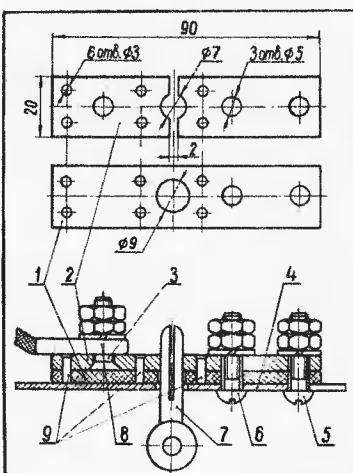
Конструкция отключателя: 1 — изоляционная пластина; 2 — медная или латунная разрезная пластина; 3 — винт подвода «минусового» провода; 4 — панель корпуса автомобиля; 5 и 6 — болты крепления; 7 — штифт; 8 — «минусовый» провод; 9 — заклепки.
